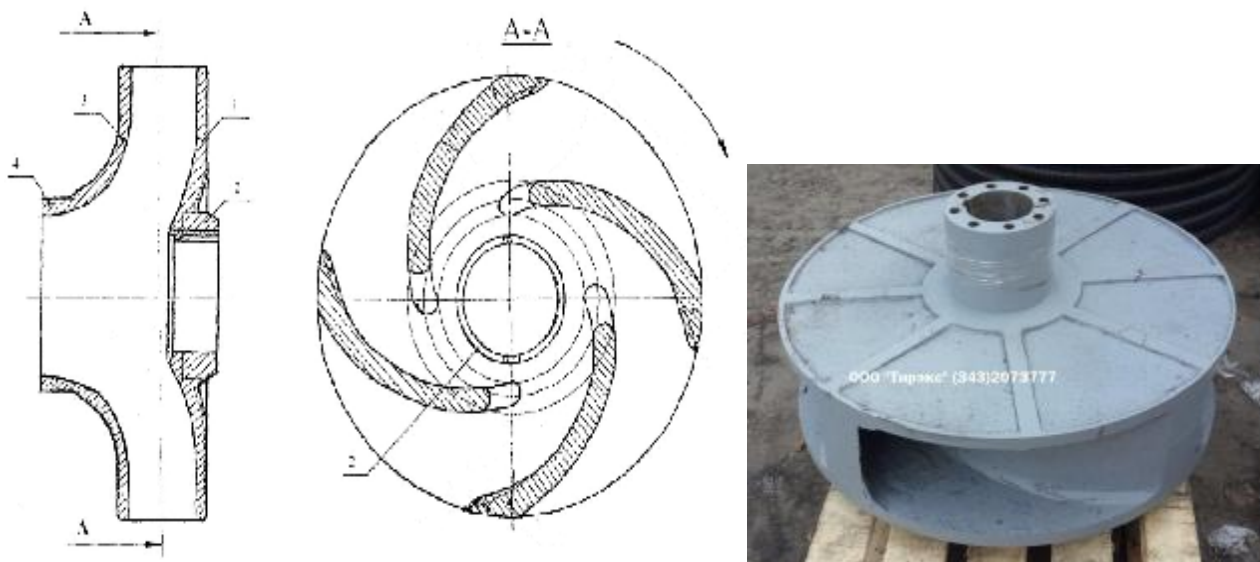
Конструкция рабочего колеса грунтового насоса
